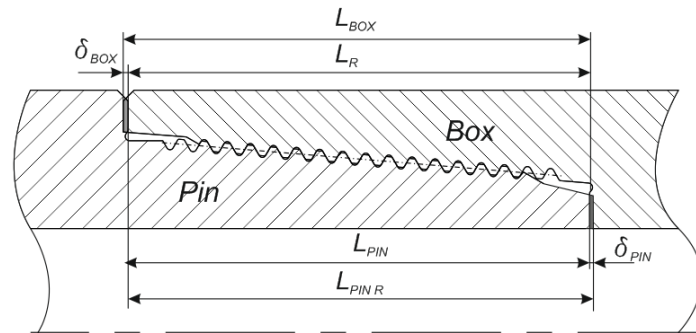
Схема двоопорного замкового з'єднання із вказаними керуючими розмірами
